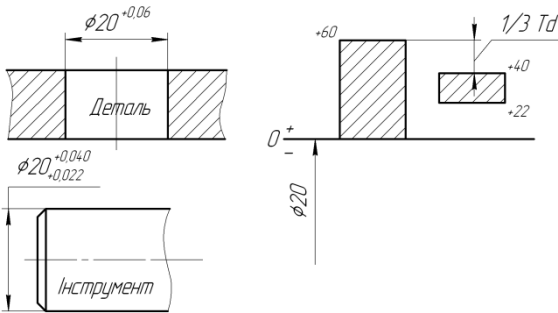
Зв'язок допуску на інструмент із допуском на розмір деталі
